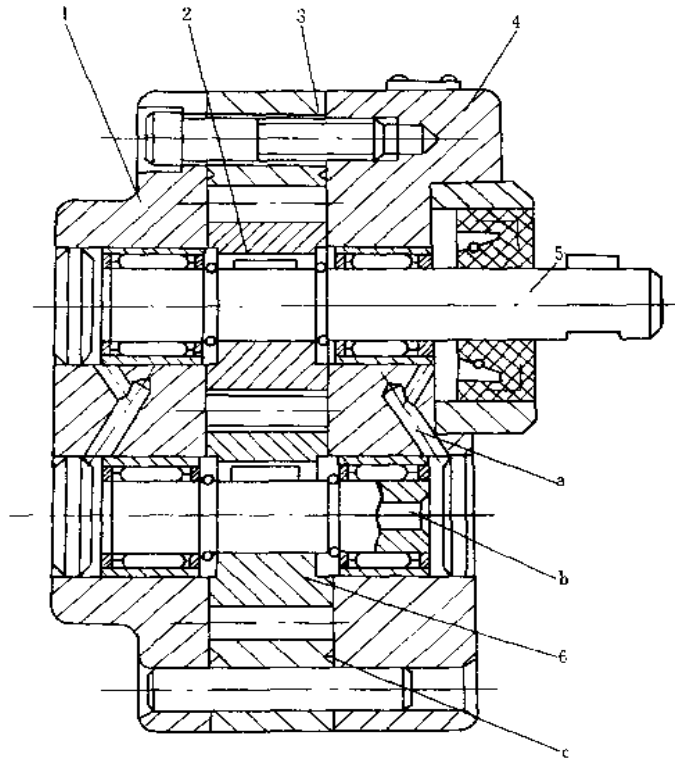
CB-B 型外啮合齿轮泵支承
